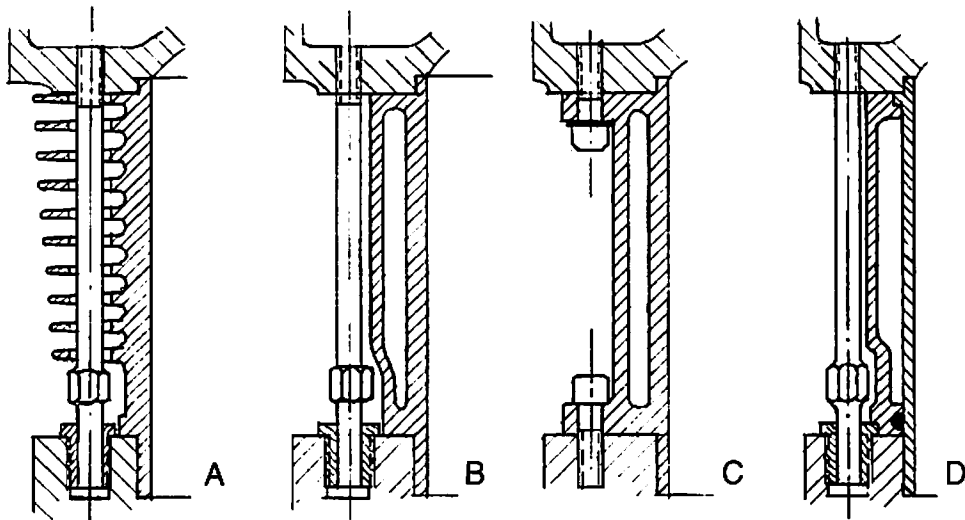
Befestigung des Zylinderkopfs am Prüfstandsmotor.
